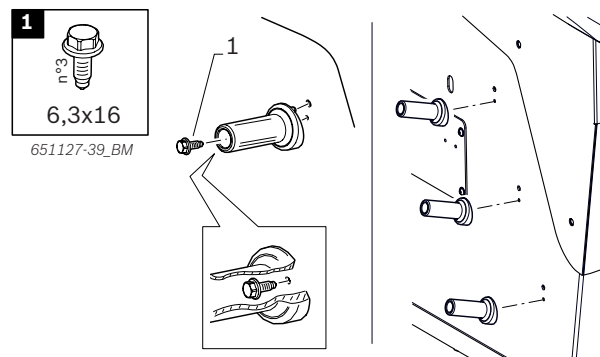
Montaggio dei supporti per dispositivi di serraggio
